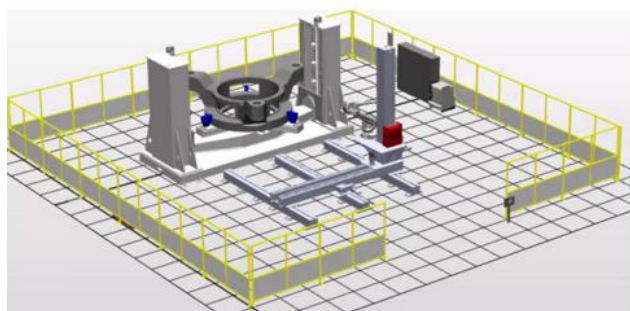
Схема компоновки сварочного роботизированного комплекса
